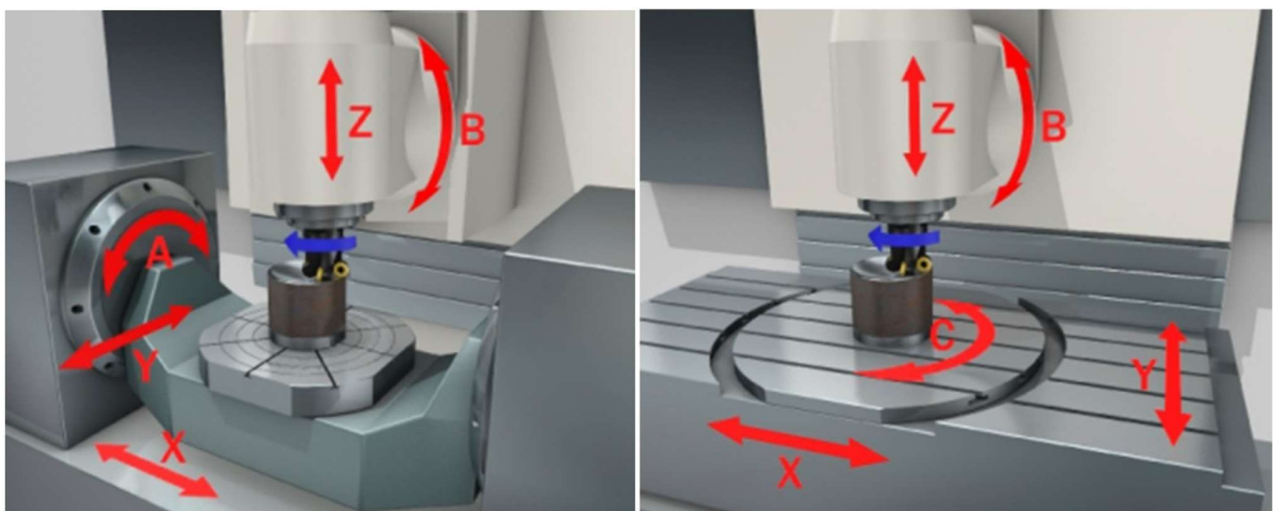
5-осьовий фрезерний обробний центр з ЧПУ
